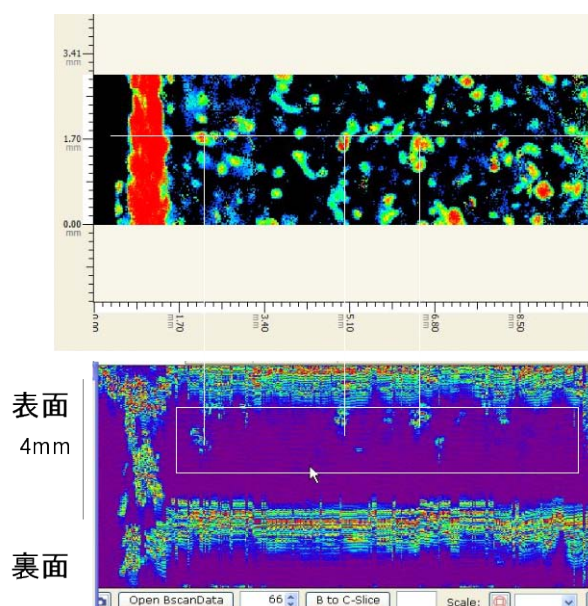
非金属介在物の非線形超音波画像（上：平面図， 下：断面図）
